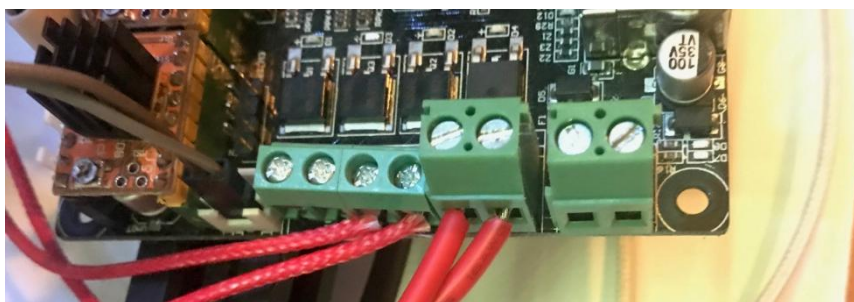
Montaje de derecha a izquierda indicando alimentación, cama y cabezal.
